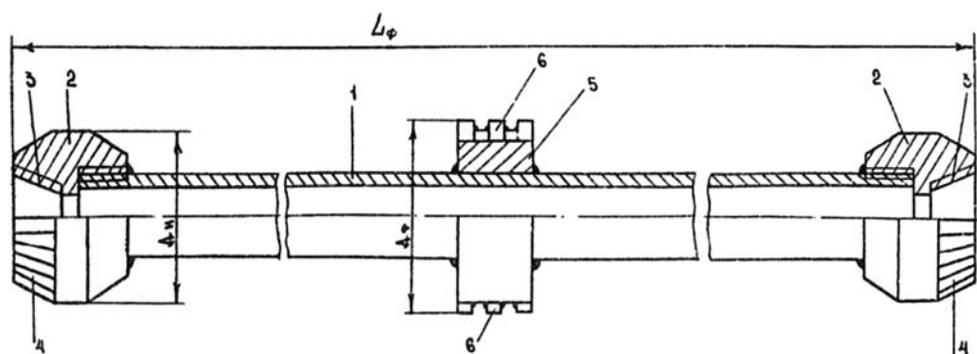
Принципиальная конструкция фрезы для ликвидации зауженных участков: 1 — бурильная труба ($D = 42-73$ мм); 2 — фрезерные направляющие; 3 — присоединительная резьба; 4 — фрезерные поверхности; 5 — фрезерный диск; 6 — твердосплавные пластины
